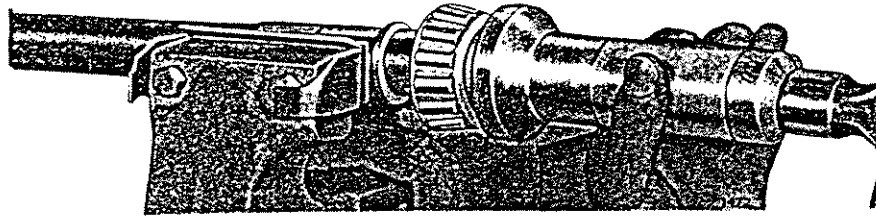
Aufdrücken des Lagers auf die Halbachse mit Werkzeug Nr. 20S.92
